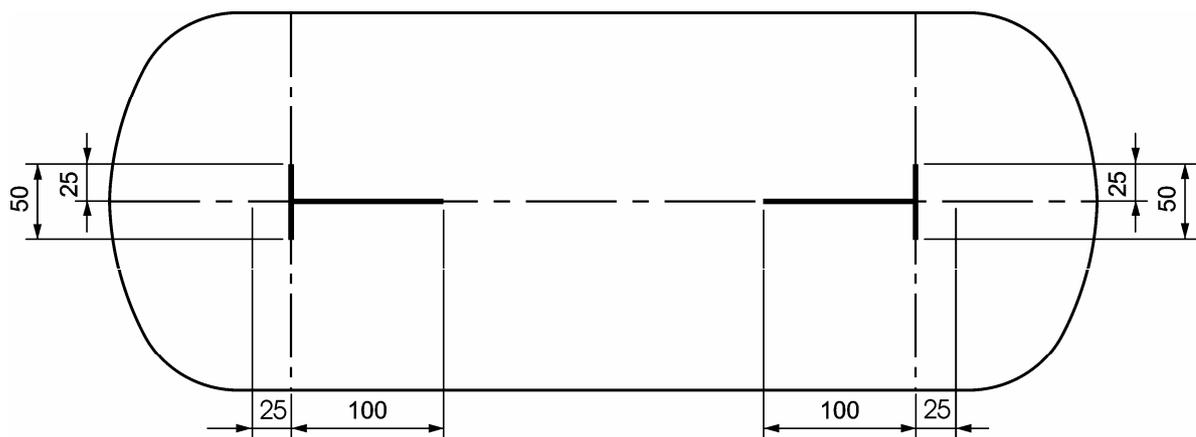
Umfang der Röntgenprüfung an Schweißnähten – Flaschen mit Rund- und Längsnahten
